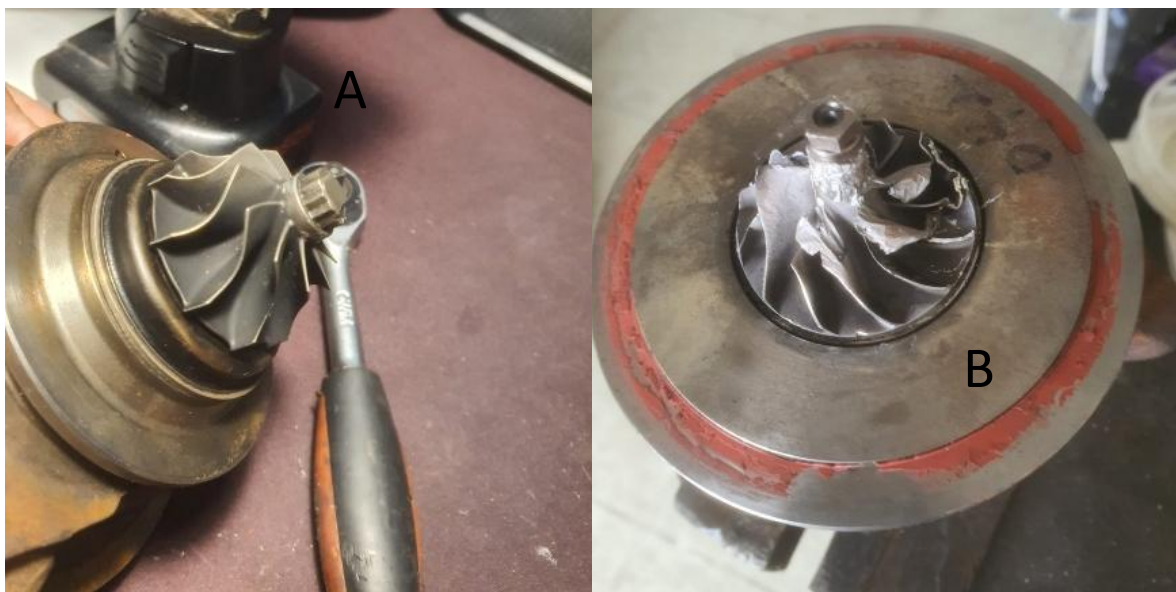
Turbina de escape (A) e de admissão (B) do turbocompressor IHI VB20
